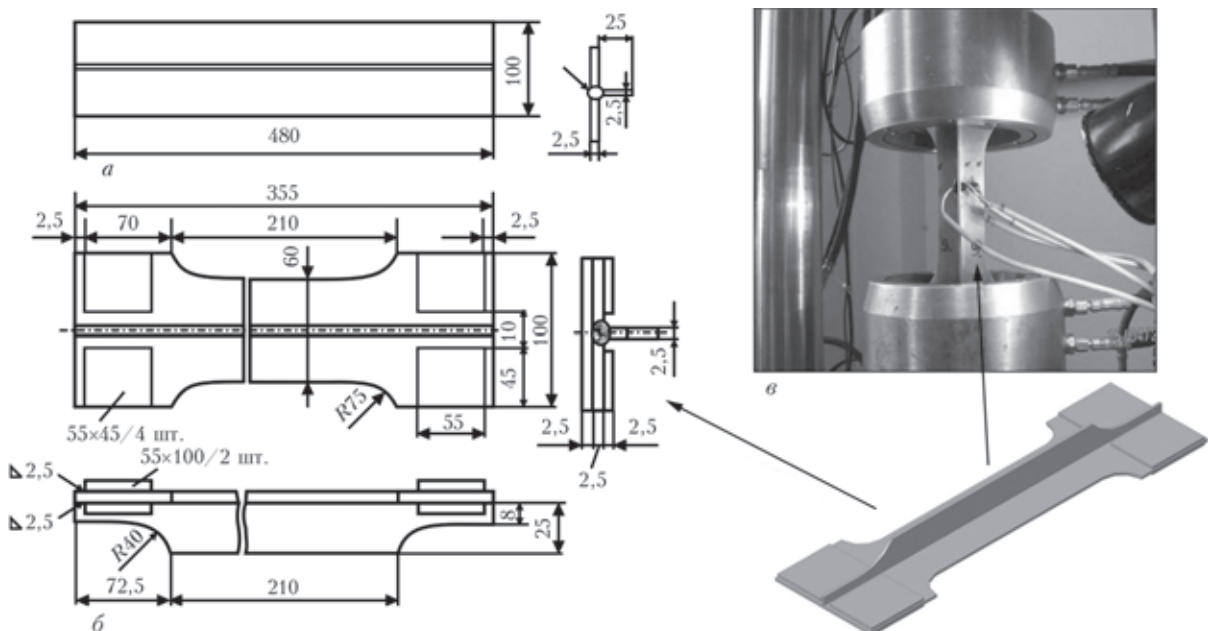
Сварной тавровый образец из сплава ВТ20 первого этапа исследований: а — эскиз образца; б — эскиз образца лопаточного типа; в — образец для испытаний на усталость, защемленный в машине
